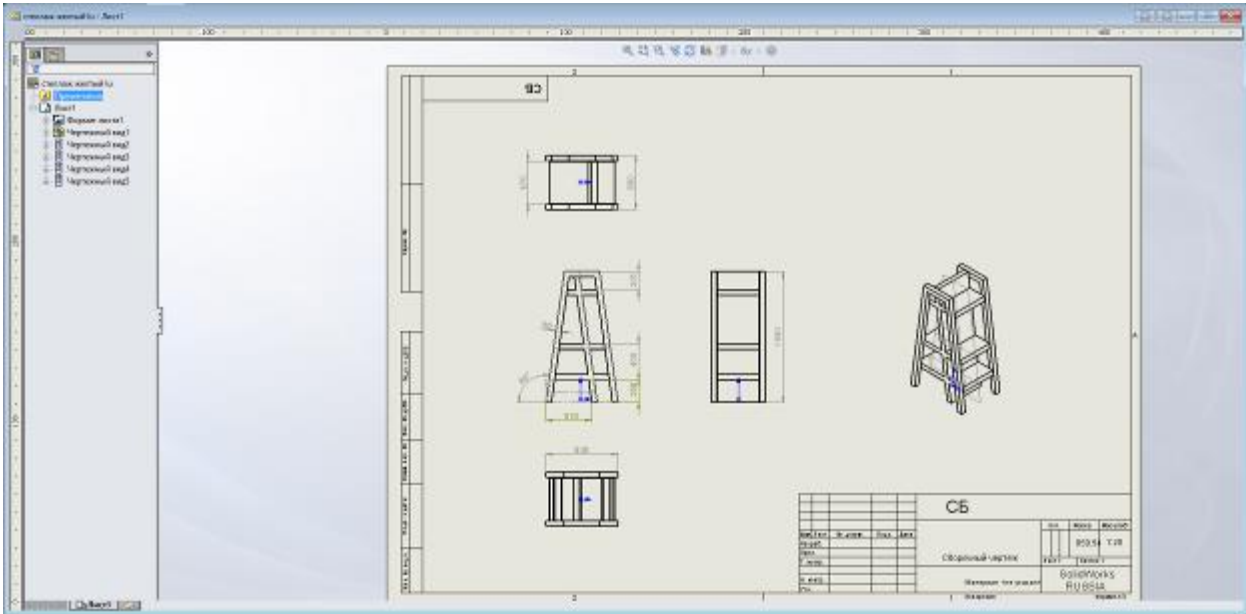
Рабочая среда сборочных чертежей SolidWorks
